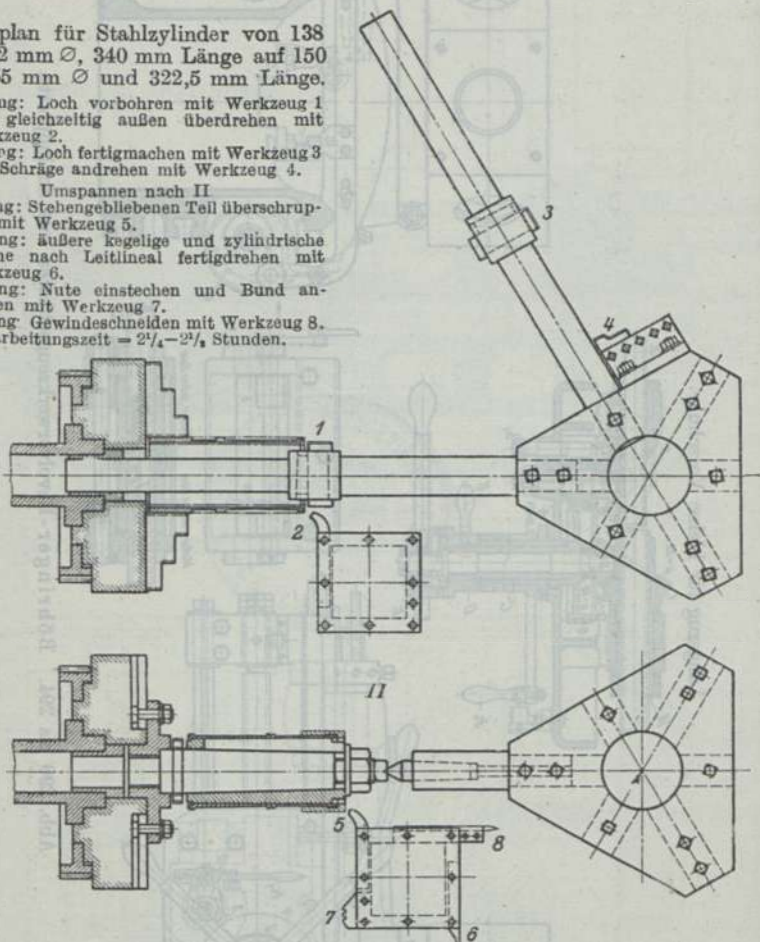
Bearbeiten von Stahlzylindern für Luftschiffmotoren.
